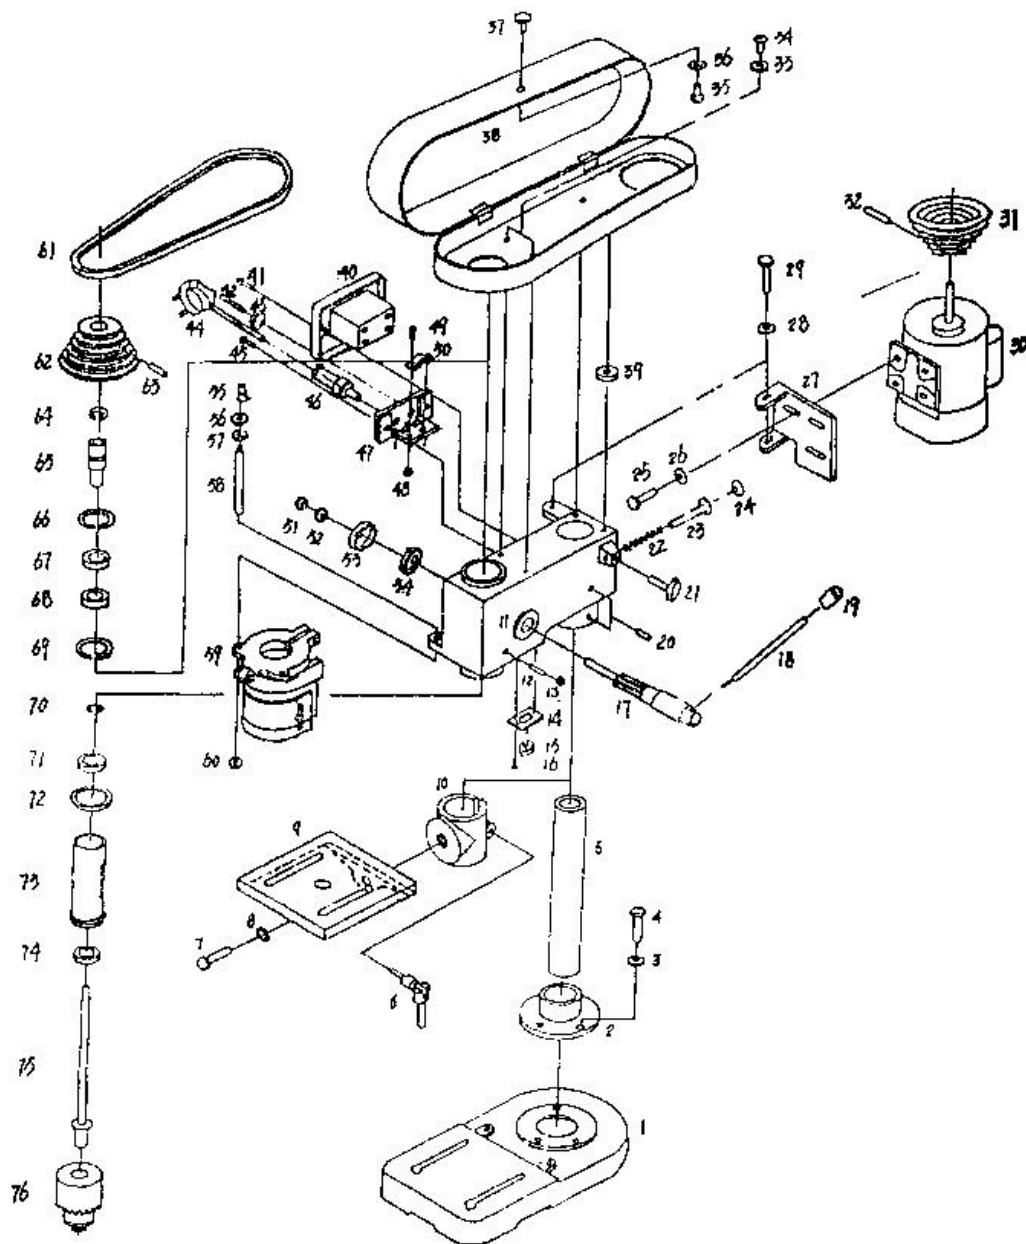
Схема свердильного станка марки KINZO 8E110.
